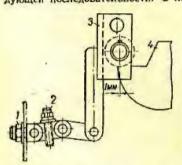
Узел для регулировки механизма включения привода типа ППМ-10:
